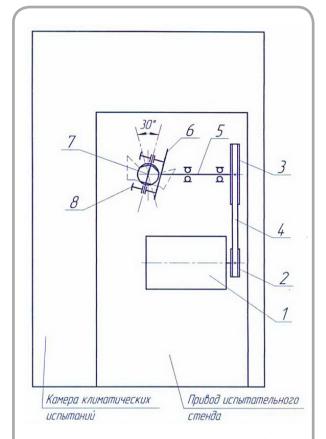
Кинематическая схема привода: 1 – электродвигатель; 2, 3 – шкив; 4 – ремень; 5 – вал упора; 6 – упор; 7 – вал поворотный; 8 – ролик вала поворотного
